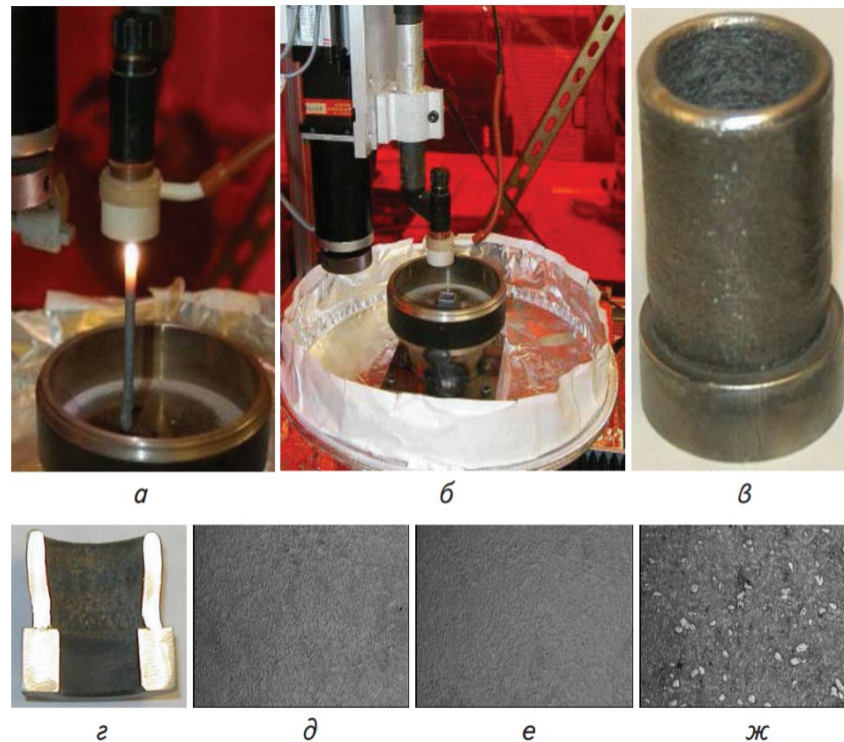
Мікроплазмове порошкове вирощування об'ємних виробів [22]: а – процес вирощування; б – лабораторна установка; в – порожнистий однорідний циліндр (інструментальна сталь H13); г – поперечний переріз циліндра з градієнтною композитною структурою (інструментальна сталь H13 + карбід вольфраму); д – структура в верхній частині циліндра; е – структура в середній частині; ж – структура в нижній частині.
